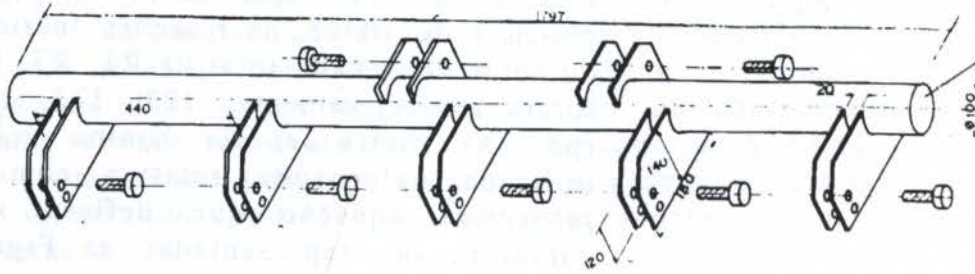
Dimensões da barra porta-ferramentas frontal (perfil tubular- mm)
